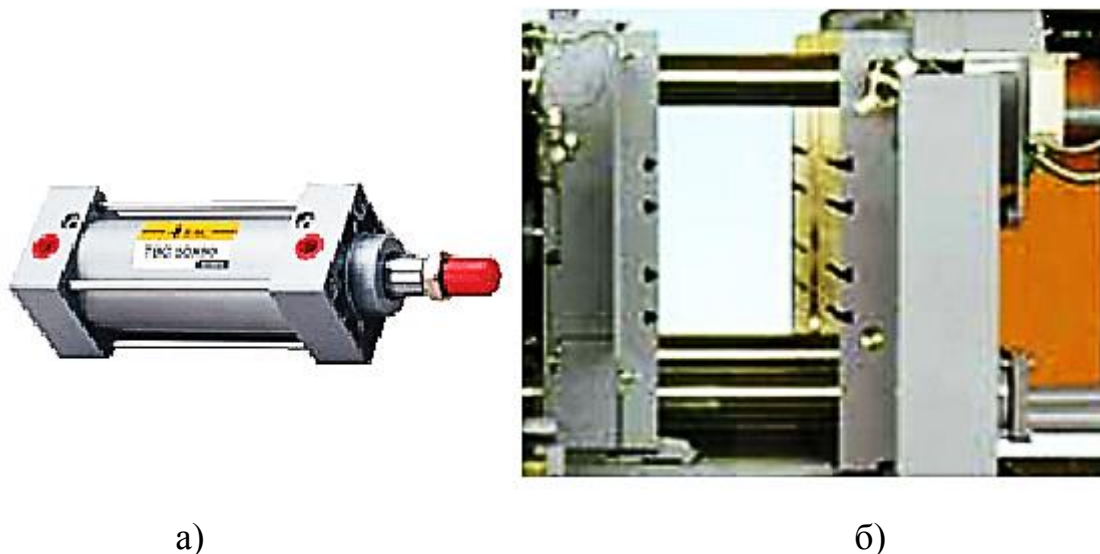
а) стандартный пневмоцилиндр выполняющий роль ресивера для создания *сжатого* воздуха; б) неподвижная и подвижная плиты горизонтальной с холодной камерой прессования литейной машины
